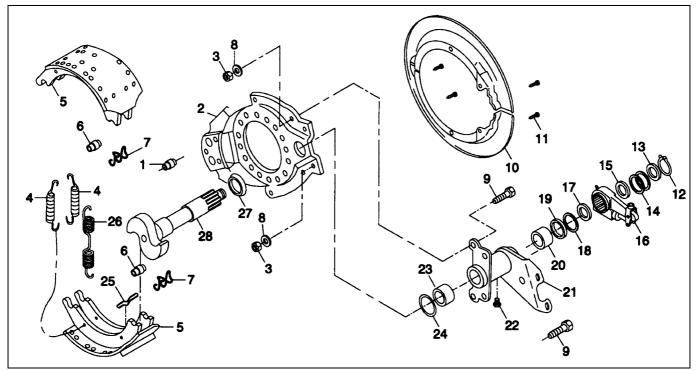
Тормоз Q Plus серии MX500 со штампованным опорным диском. 1 - анкерный палец, 2 - опорный диск, 3 - гайка (4 шт.), 4 - фиксирующая пружина, 5 - тормозная колодка в сборе, 6 - ролик кулачка, 7 - клипса ролика, 8 - закаленная шайба (4 шт.), 9 - болт (4 шт.), 10 - пыльник, 11 - болт пыльника, 12 - стопорное кольцо кулачкового вала, 13 - шайба/проставка, 14 - тонкая проставка, 15 - оранжевый сальник, 16 - автоматический компенсатор износа, 17 - сальник 18 - толстая проставка, 19 - сальник, 20 - втулка кулачкового вала (1-1/2 дюйма), 21 - кронштейн кулачкового вала и тормозной камеры, 22 - пробка, 23 - втулка кулачкового вала (1-5/8 дюйма), 24 - оранжевый сальник, 25 - палец возвратной пружины, 26 - возвратная пружина, 27 - упорная шайба с фаской, 28 - кулачковый вал.
